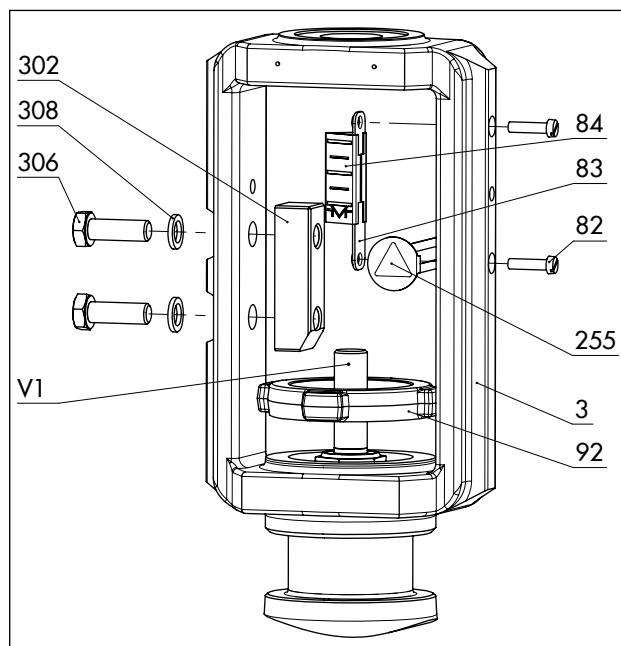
Montaje del puente con placa indicadora de carrera en la ejecución especial
